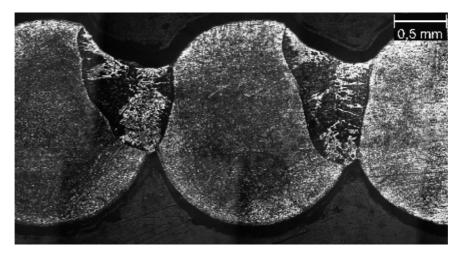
Общий вид области сварного шва пружинно-витого канала, полученного сваркой непрерывным лазерным излучением
